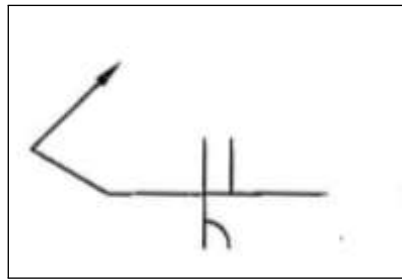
Aplicación de Símbolos de soldaduras asimétricos
